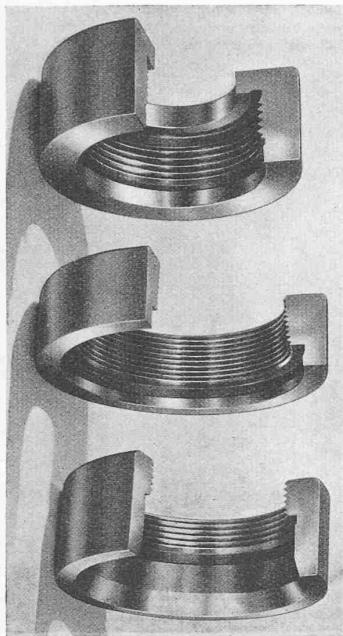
Werkstücke, deren Innengewinde, Bohrungen und Planflächen auf der Maschine Typ RI (Abb. 2) in einer Aufspannung fertig geschliffen wurden
